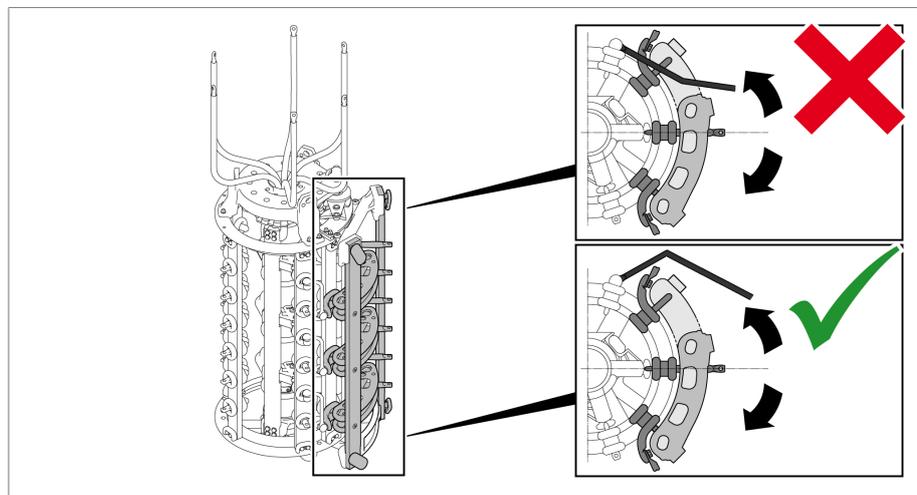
Присоединительные контакты преобразователя при переключении с реверсом (вид сверху)
